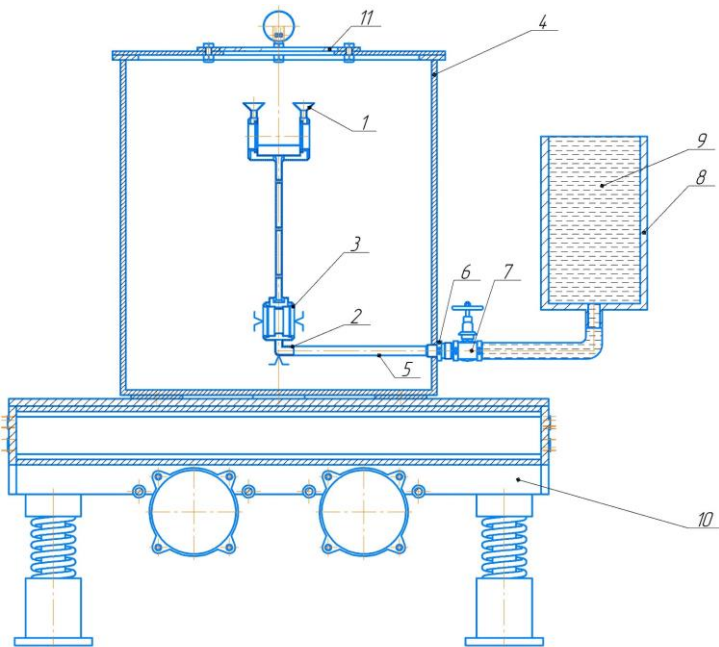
Технологическое обеспечение для реализации способа изготовления композитных деталей: 1 - выпор; 2 - литник; 3 – оболочковая форма; 4 – вакуум-камера; 5 – трубопровод; 6 – штуцер; 7 – кран; 8 – бункер; 9 – металлополимер; 10 – вибростол; 11 – смотровое окно; 12 – композитная деталь.
